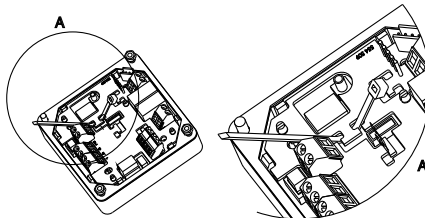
Einsatz der Kabelschellen bei Ausführungen ohne EN 175301-803-Stecker
